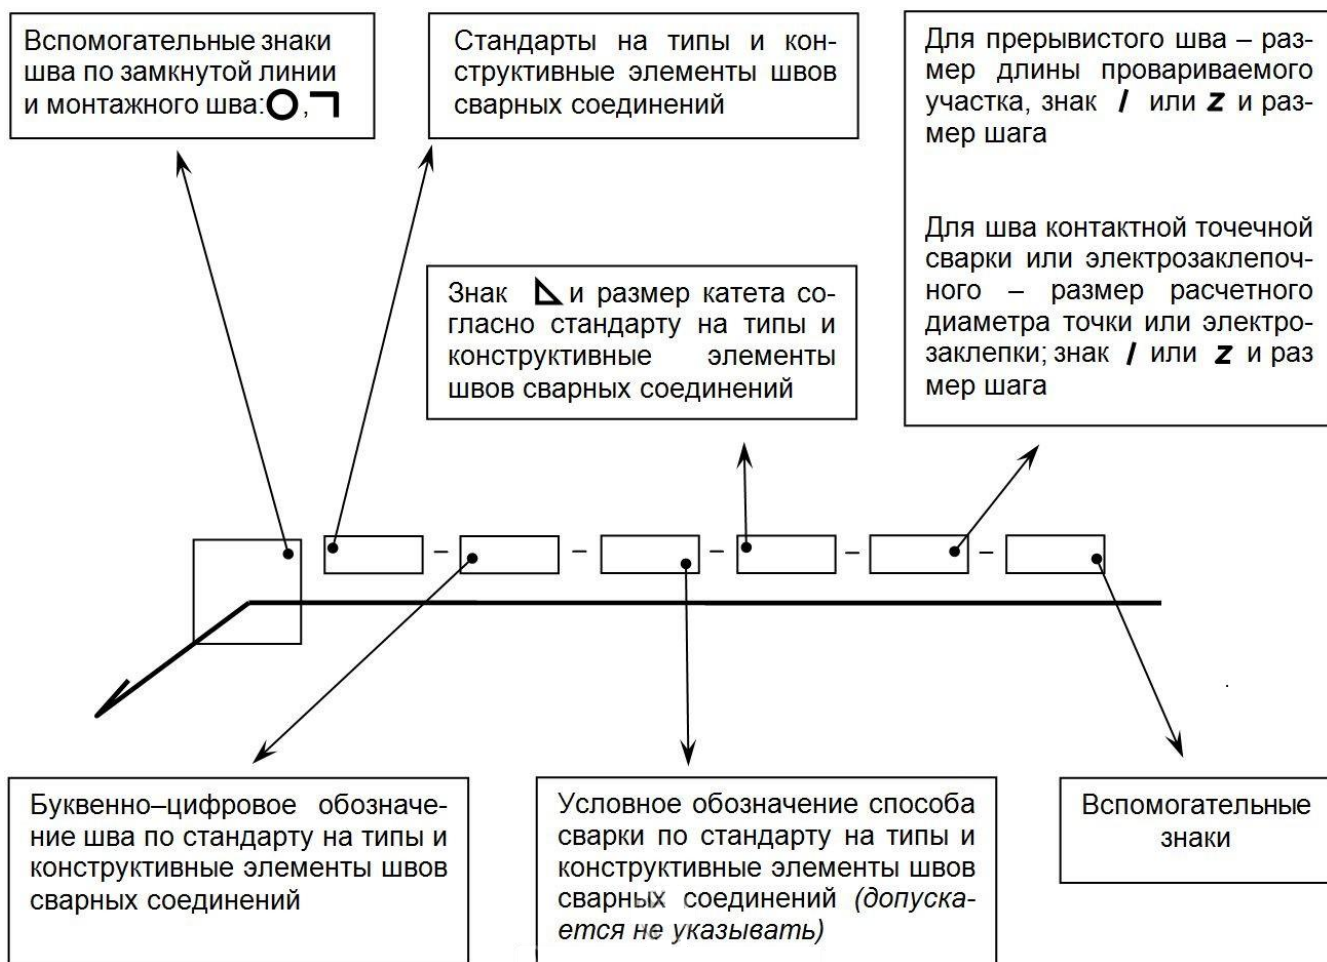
Структура условного обозначения сварного шва
